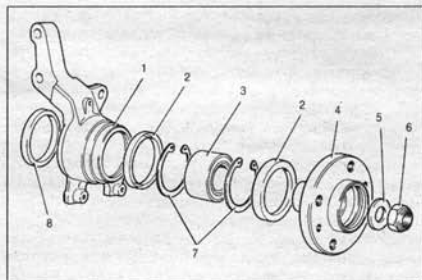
Поворотный кулак и детали ступицы переднего колеса: 1 – поворотный кулак; 2 – наружное грязеотражательное кольцо; 3 – подшипник ступицы; 4 – ступица колеса; 5 – упорная шайба; 6 – гайка; 7 – стопорное кольцо; 8 – внутреннее грязеотражательное кольцо
